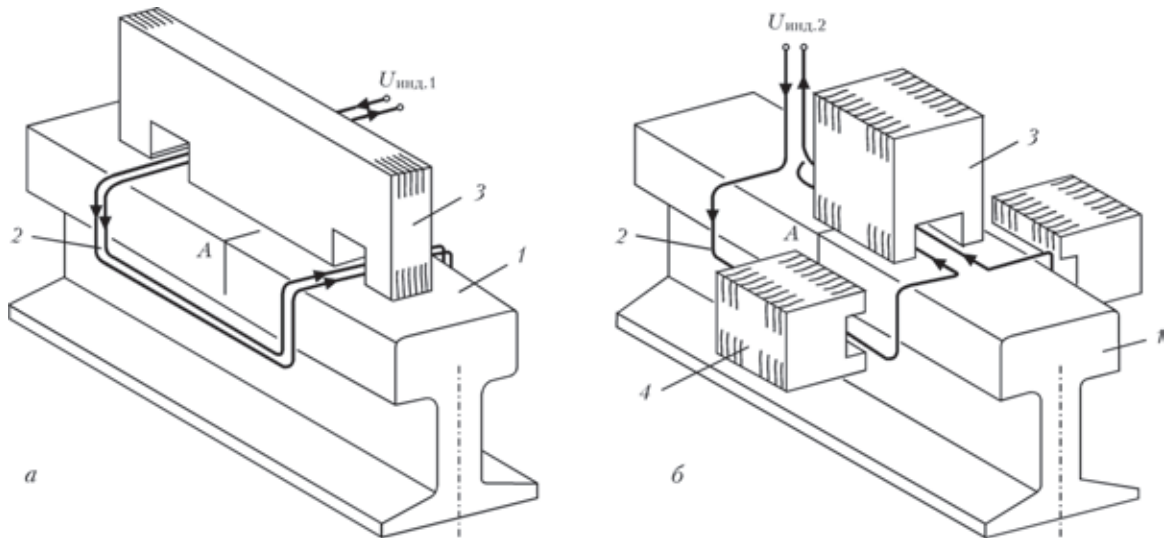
Конструкции индукторов 1 (а) и 2 (б) для нагрева головки рельса: 1 — рельс типа Р65; 2 — индуктирующий провод; 3 — основной магнитопровод; 4 — дополнительные магнитопроводы
